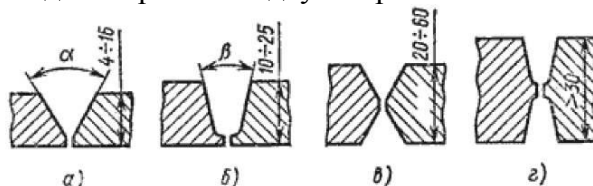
Формы подготовки кромок под сварку:
